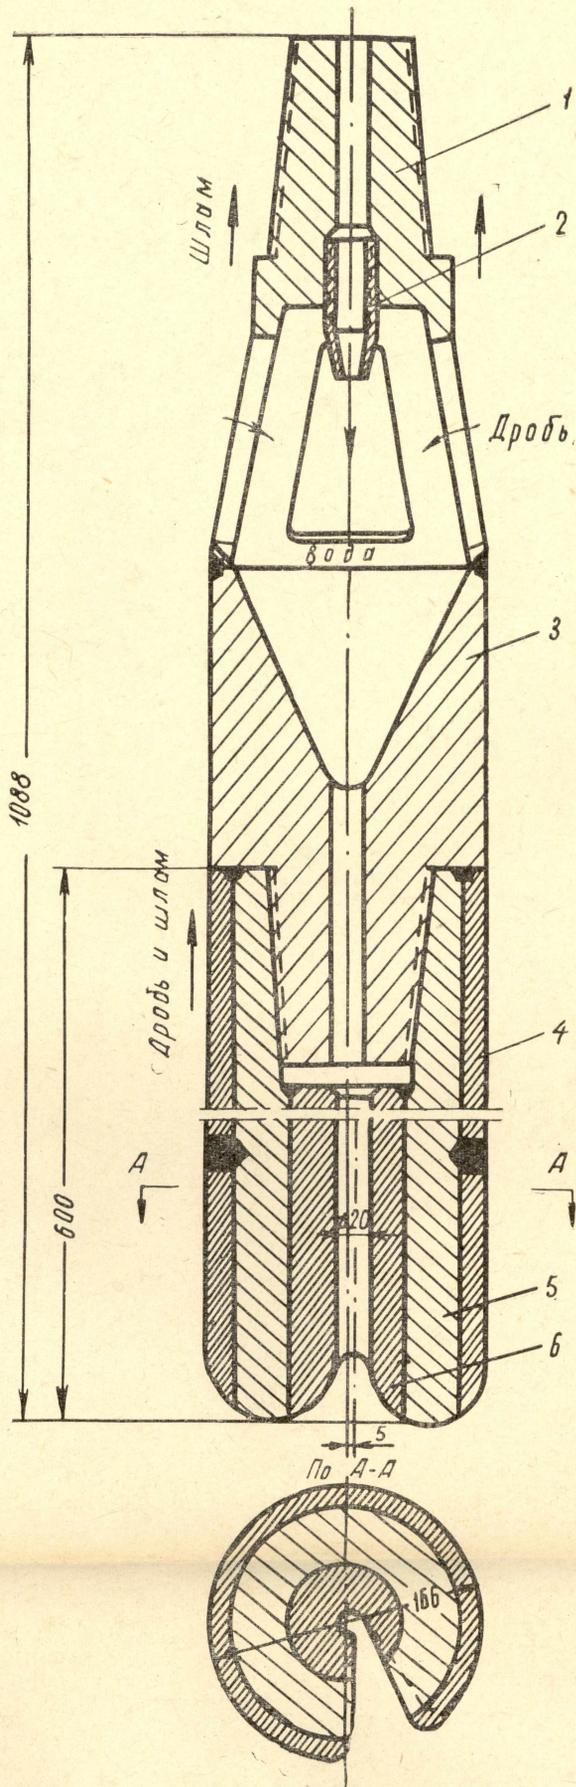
Дробовая коронка для бурения сплошным забоем: 1 — верхняя часть корпуса; 2 — гидравлическая насадка; 3 — нижняя часть корпуса; 4 — коронка; 5 и 6 — втулки
